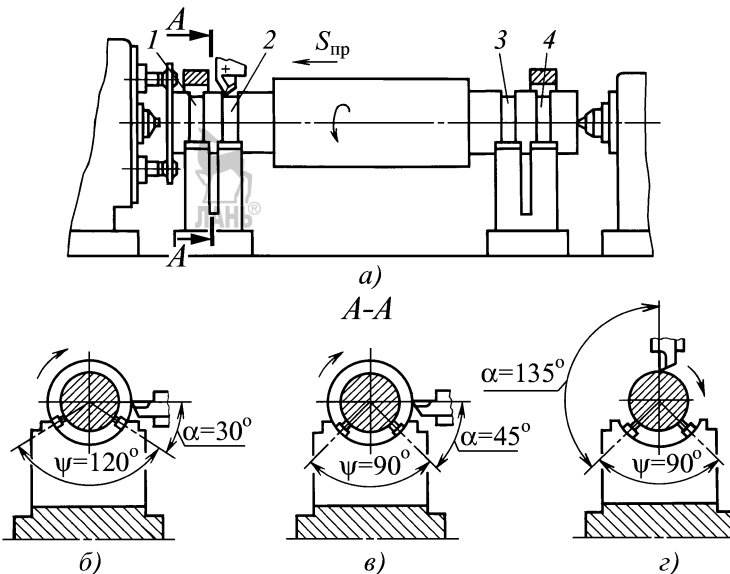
Схемы (а) бесцентровой обработки валков в двухопорных люнетах и расположения вкладышей люнета и резца (б–г)
